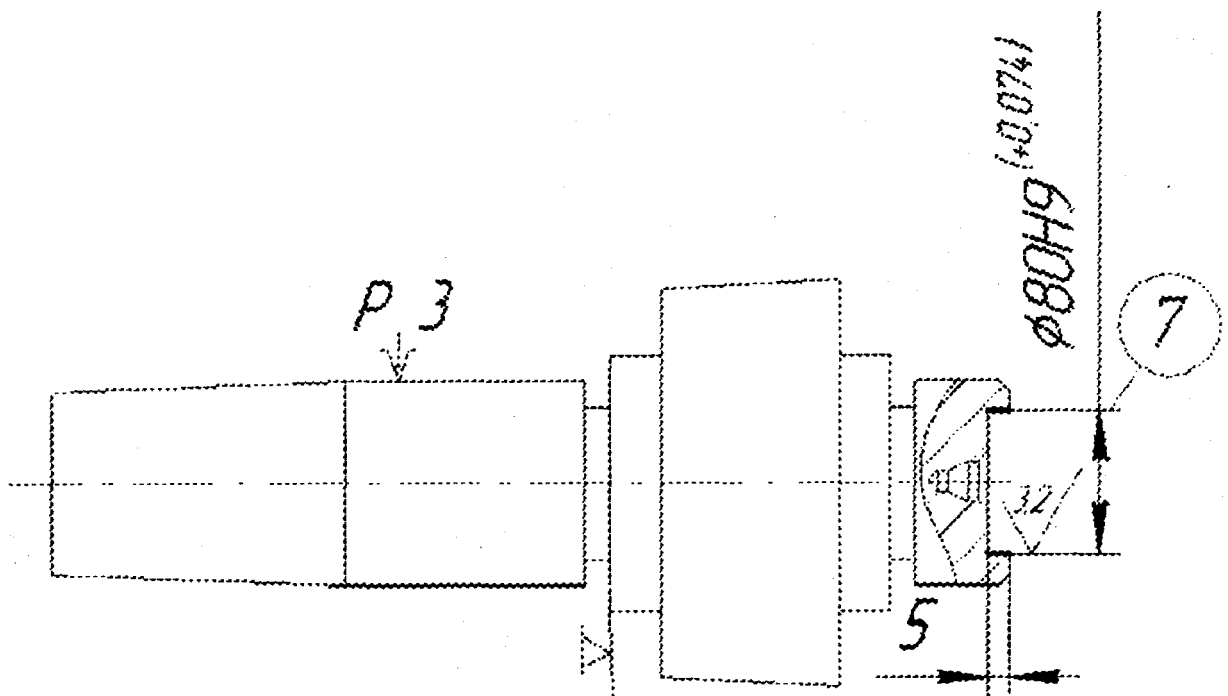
Ескіз обробки внутрішньої циліндричної поверхні Ø80H9 (+0,074)
